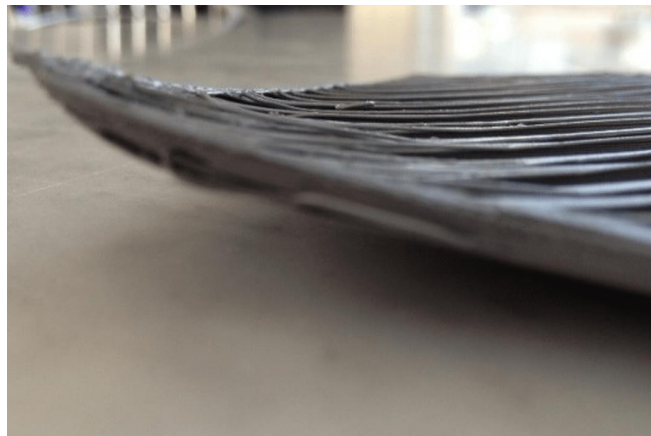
Pieza fabricada mediante impresión 3D con efecto warping. [20]
